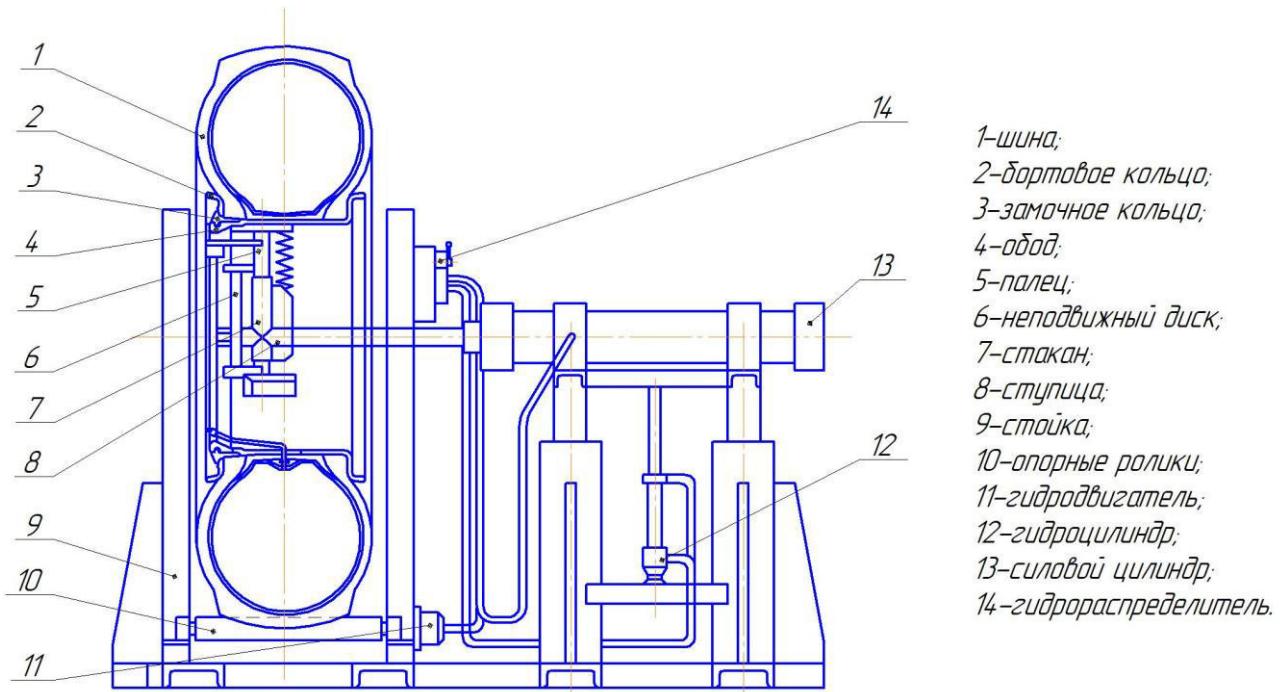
Стенд для разборки и сборки бездисковых колес
